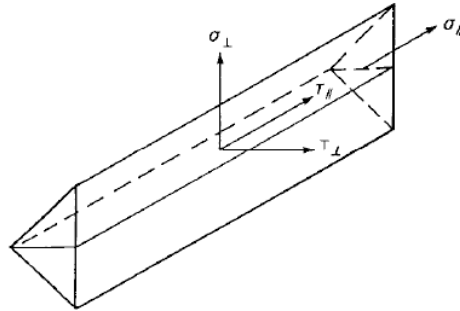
Tensiones sobre la sección de garganta de un cordón de una soldadura en ángulo
